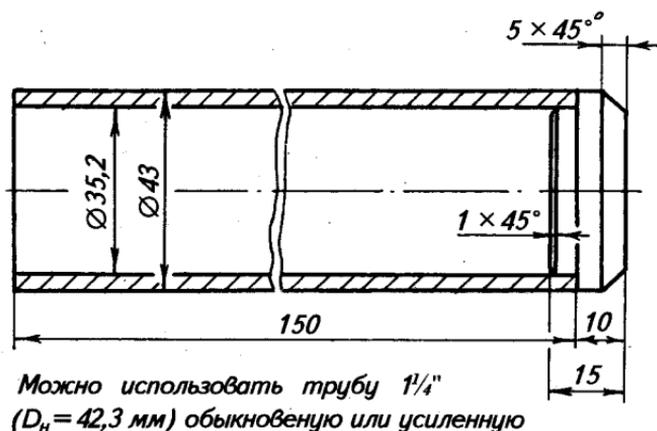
Оправка для запрессовывания внутреннего кольца внутреннего подшипника.
